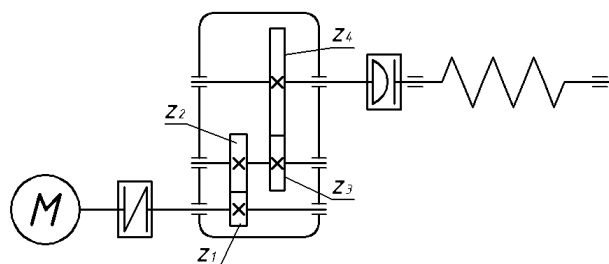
Кинематическая схема привода винтового конвейера
